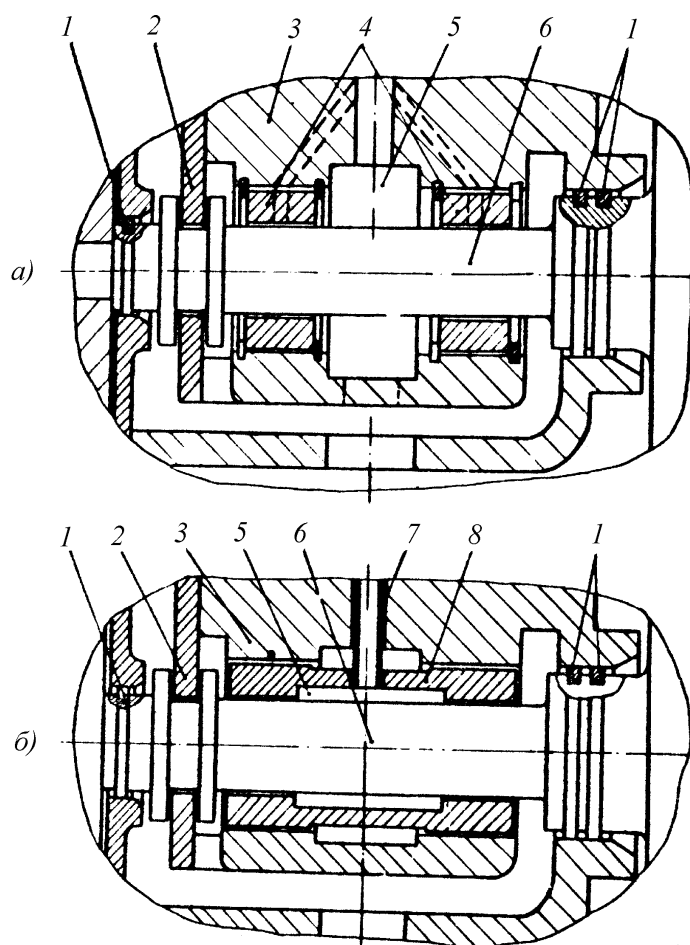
Типичные конструкции узлов подшипников турбокомпрессора:
